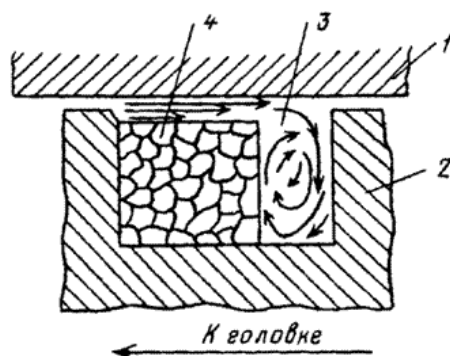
Схема плавения пробки материала в зоне II в межвитковом сечении шнека: 1 – стенки цилиндра; 2 – гребень шнека; 3 – потоки расплава полимера; 4 – спрессованный твердый полимер (пробка) в экструдере.
